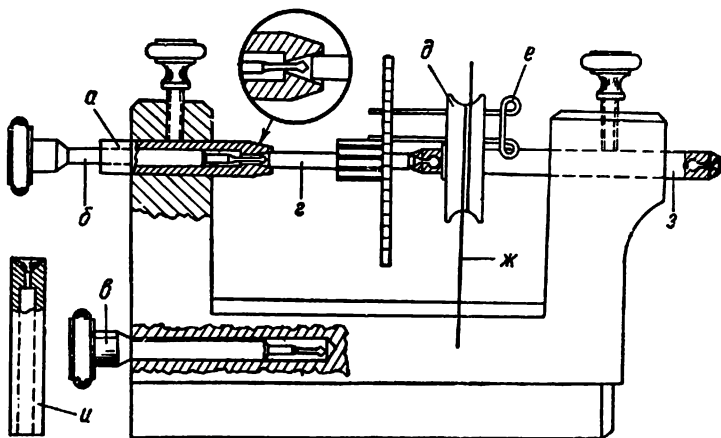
Машинка для сверления: *а* — передний центр; *б* — сверло; *в* — запасное сверло; *г* — ось промежуточного колеса; *д* — ролик; *е* — поводок; *ж* — смывок; *з* — задний центр; *и* — запасной центр для крупных работ
